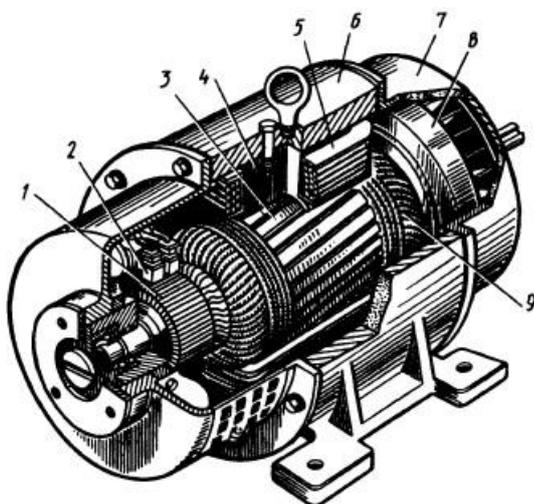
Устройство машины постоянного тока: 1 – коллектор; 2 – щетки; 3 – сердечник якоря; 4 – главный полюс; 5 – катушки обмотки возбуждения; 6 – корпус (станина); 7 – подшипниковый щит; 8 – вентилятор; 9 – обмотка якоря
